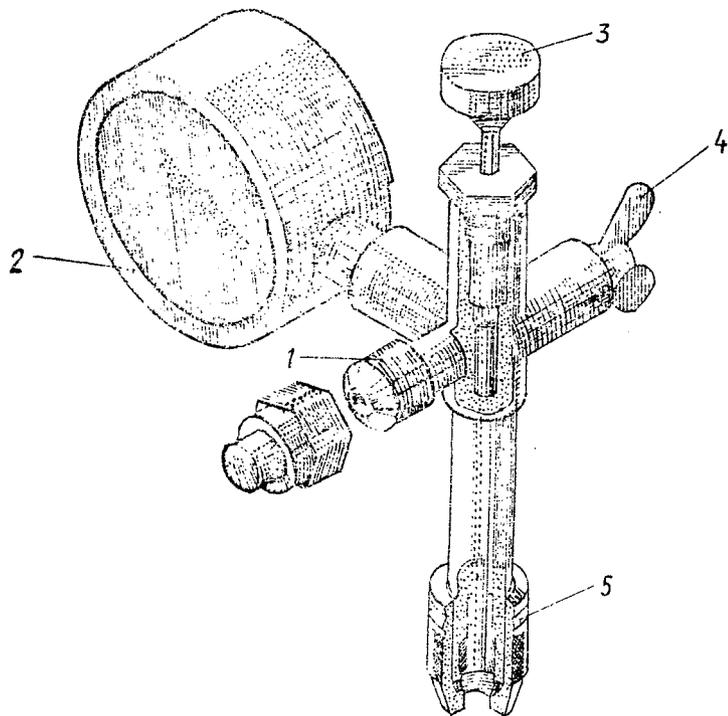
Приспособление 24-9211-0 для зарядки шин:
